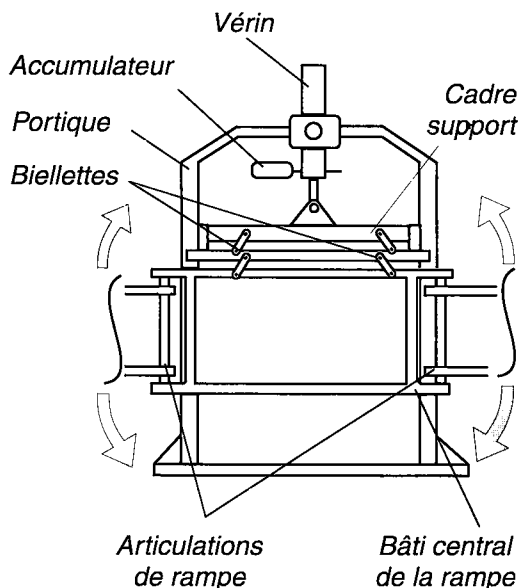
Dispositif de stabilisation d'une rampe par deux niveaux de biellettes
